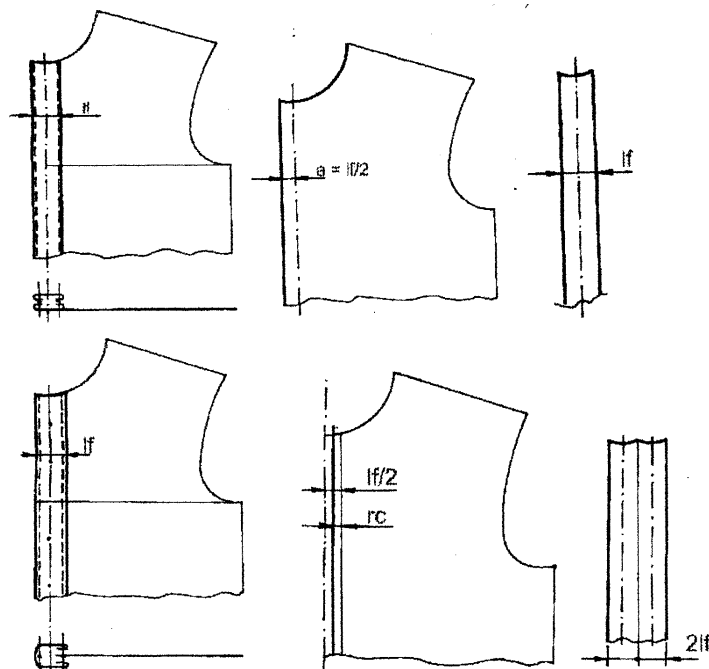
Construcția închiderii cu marginile croite separat.
